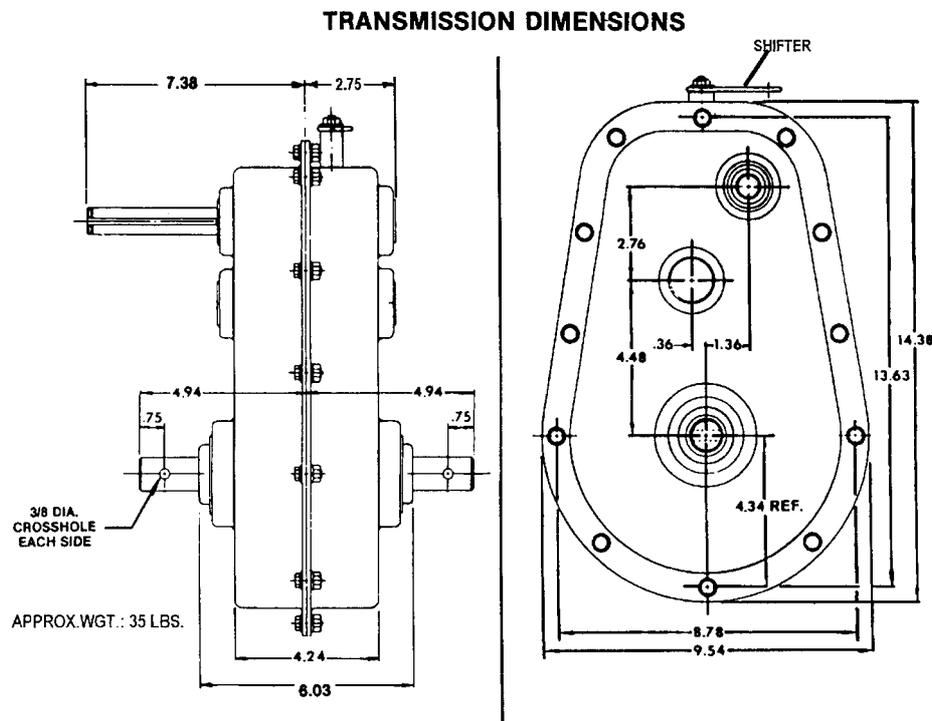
Dimensiones del reductor de giro transaxel cutaway, medidas en pulgadas.
